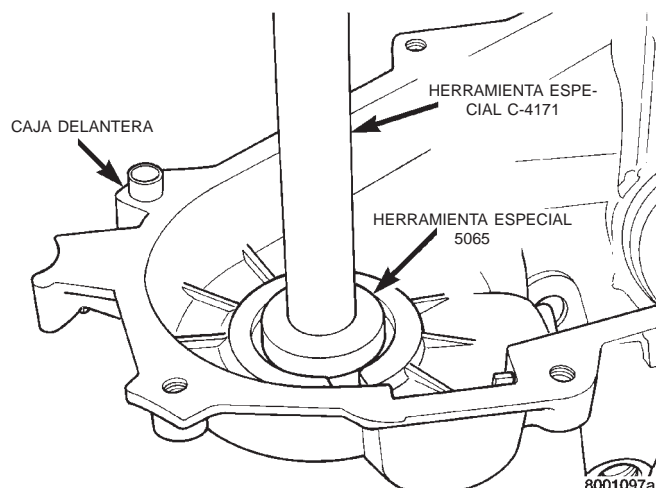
Desmontaje de cojinete del eje transmisor delantero
